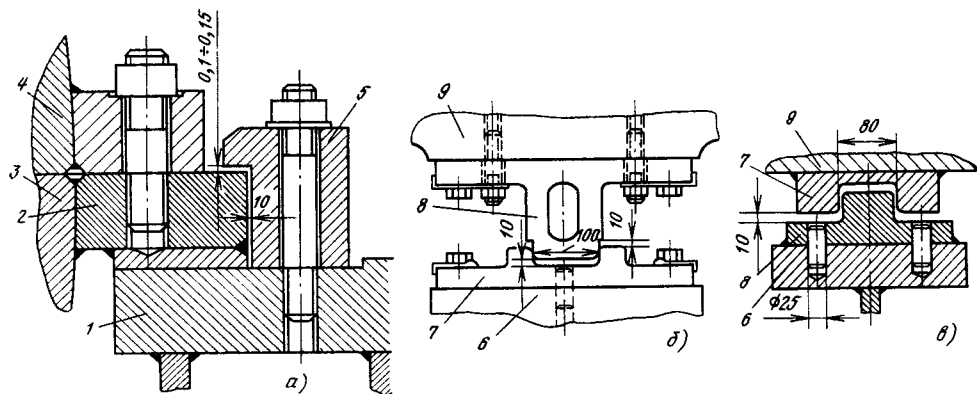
Детали установки обоймы в корпусе ЦНД:
